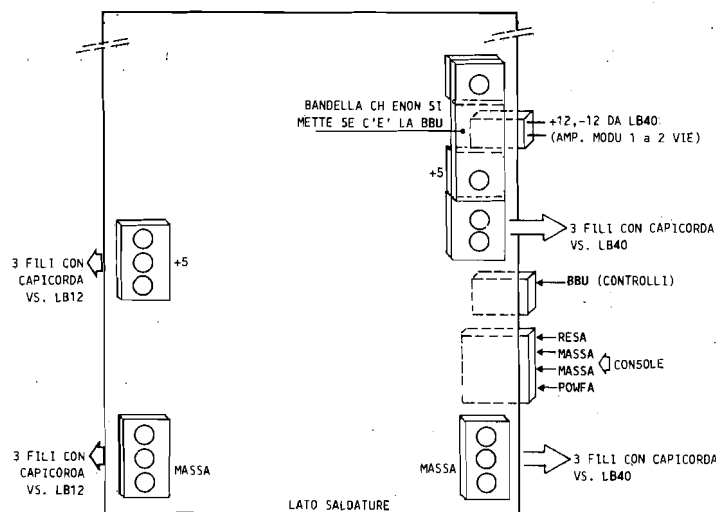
Vista posteriore del BACK PLANE e dei suoi connettori
